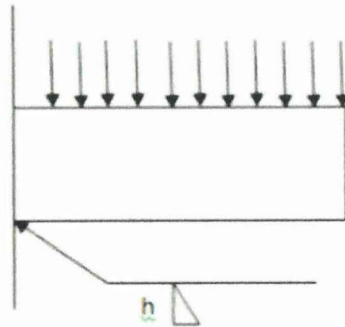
Esquema de un voladizo unido por soldaduras a un soporte vertical
